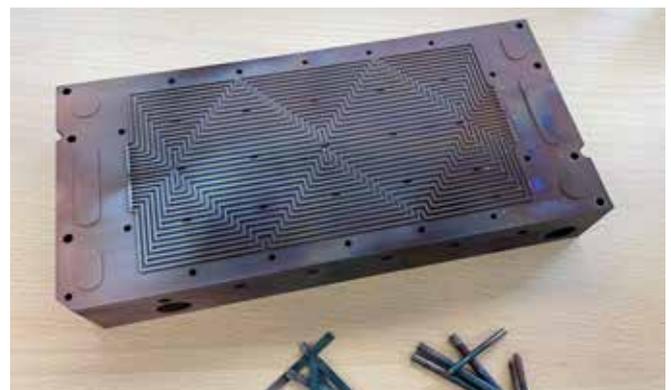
beschichteter Werkzeugeinsatz mit Stiften zum Verschließen der Auswerferbohrungen
